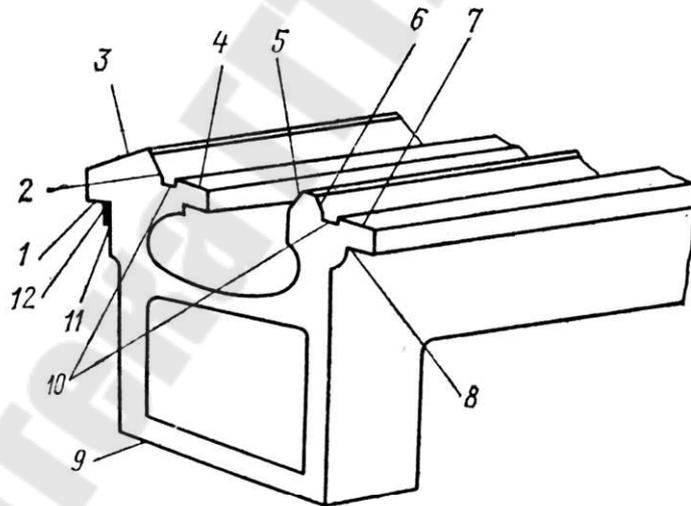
Направляющие станины токарно-винторезного станка модели 1А62
